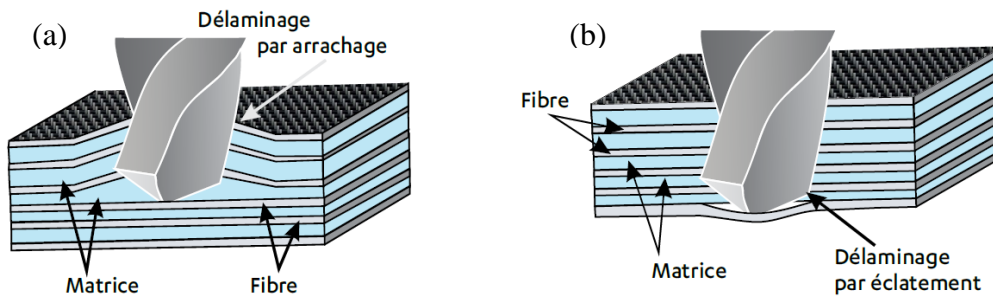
Deux types de délaminage à cause de perçage : (a) Délaminage par arrachage ; (b) Délaminage par éclatement
